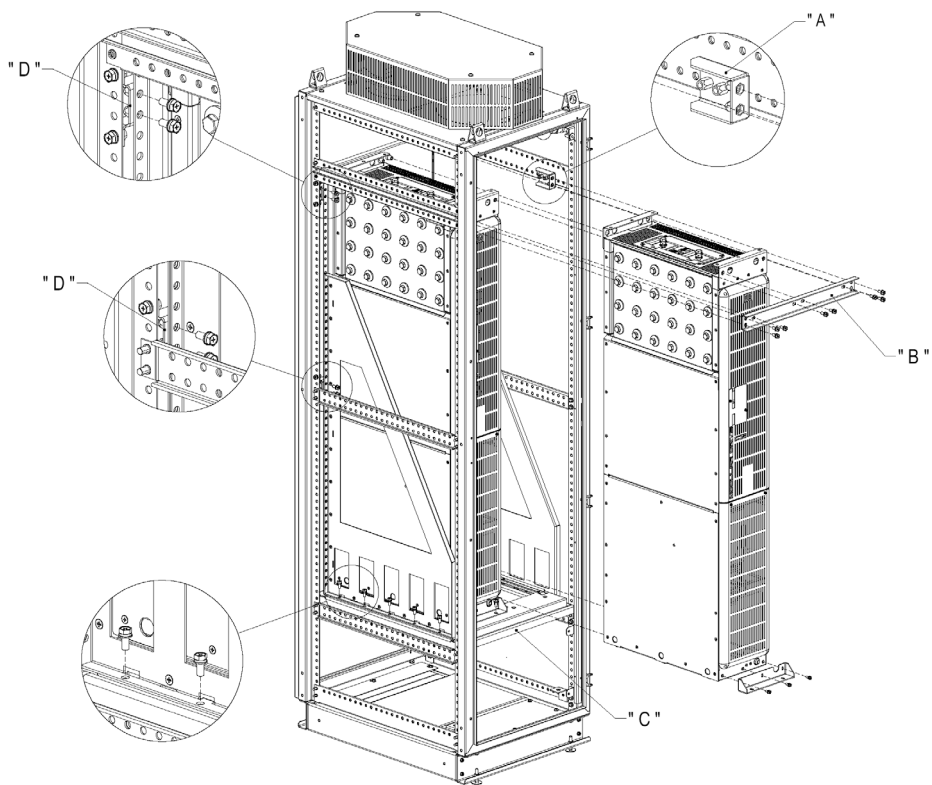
Detalles de montaje del Rack 2 en armario (tablero) con 600 mm de ancho
